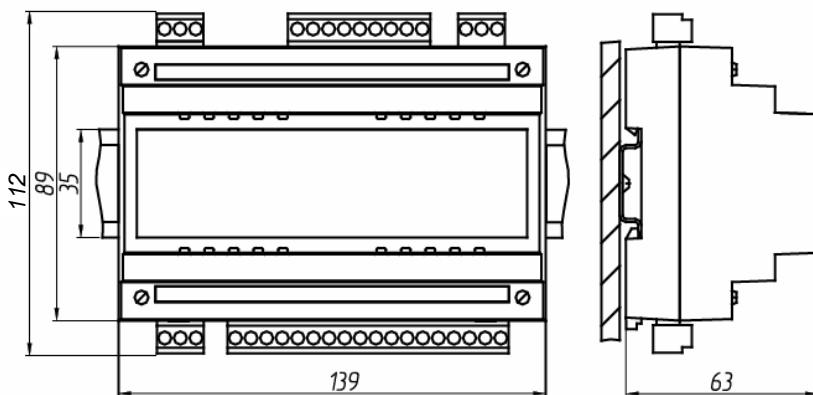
Габаритно-присоединительные размеры счетчика
